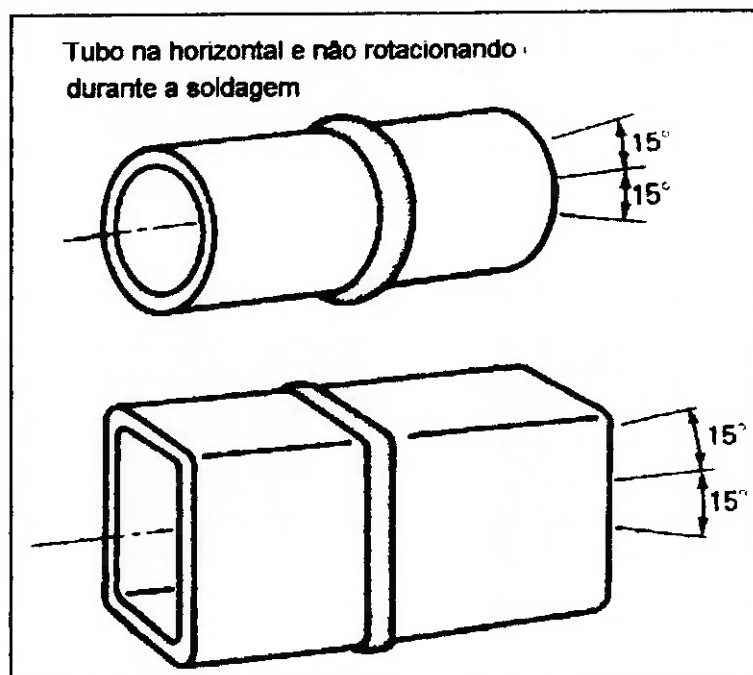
Posição de teste 5G para tubos conforme AWS D1.1^[14]
